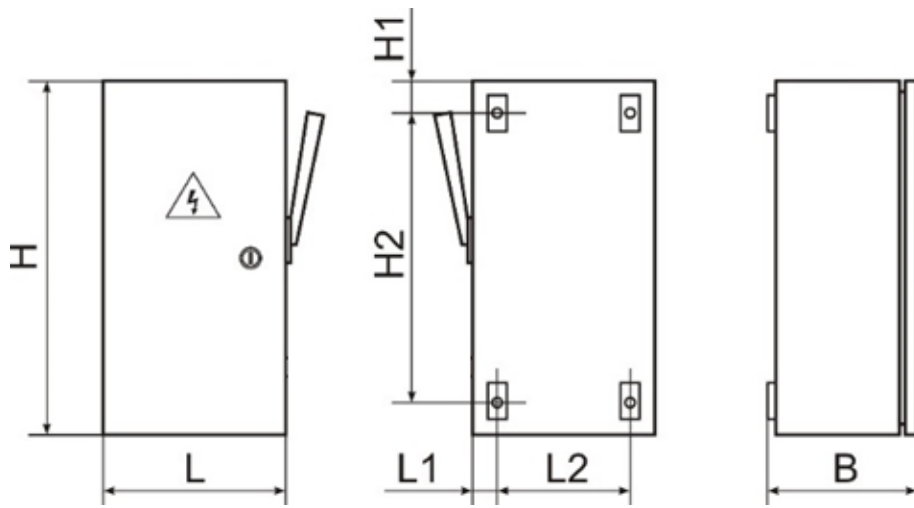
Общий вид и габаритные размеры ЯБПВУ-М
